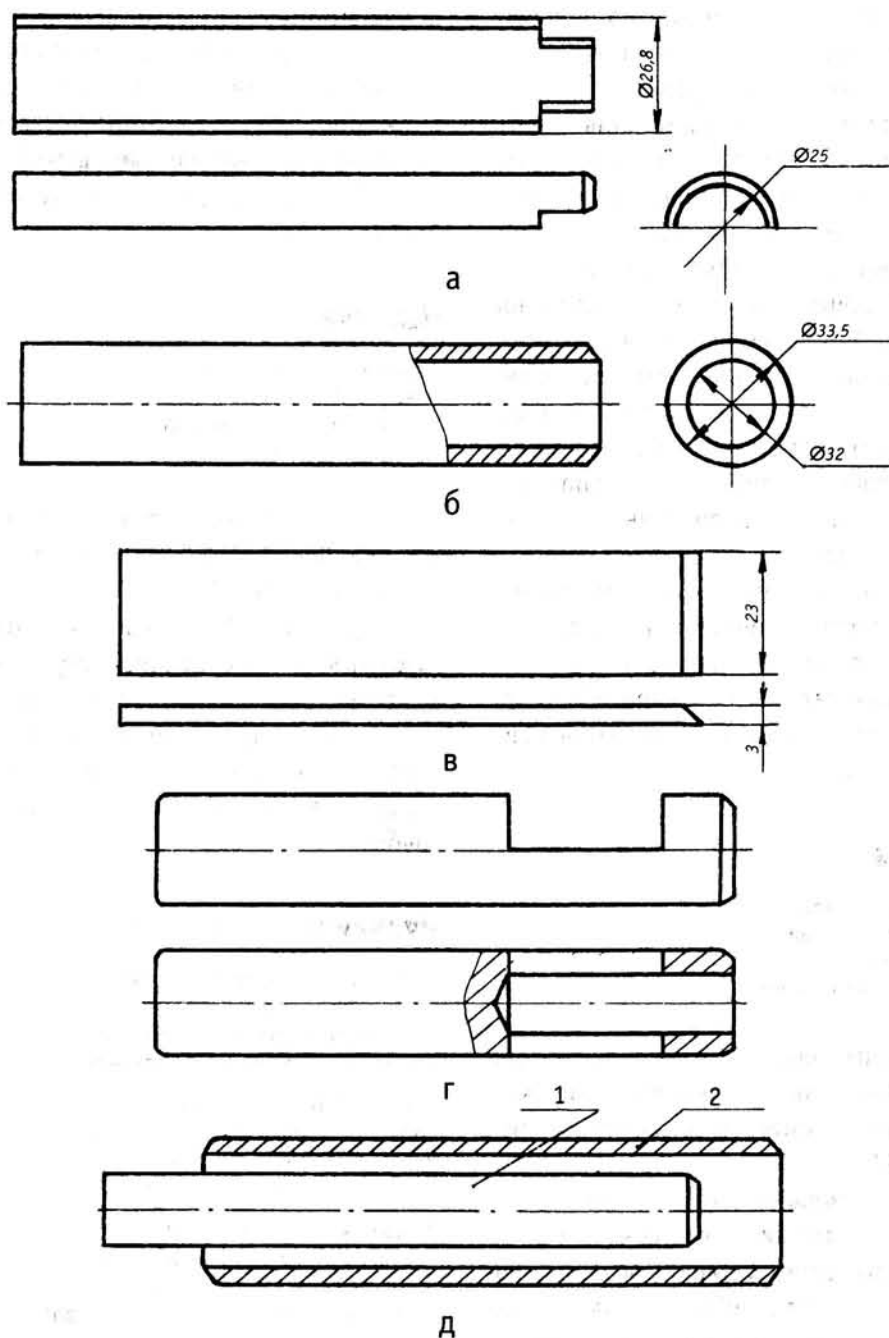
Просечки стальные: а, б, в — для прокладок к смесителю типа «Елочка»; г — выточена на токарном станке для прокладок к вентильным головкам и вентилям; д — из стальной трубки для прокладок к вентильным головкам и вентилям: 1 — трубка или стержень для выталкивания прокладок из просечки; 2 — просечка
